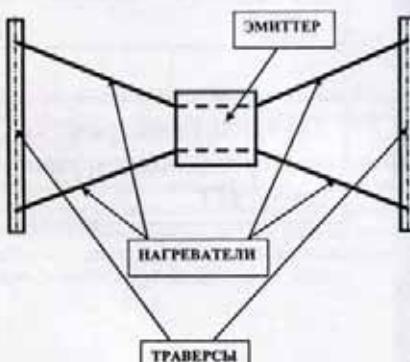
Кинематическая схема установки приварки траверс к нагревателям
